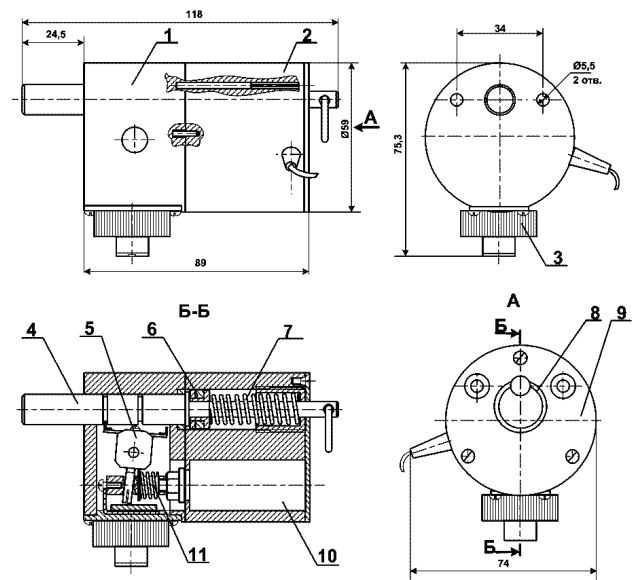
Конструкция: 1 – основание, 2 – цилиндр, 3 – устройство аварийного деблокирования, 4 – шток, 5 – механизм блокировки, 6 – магнит, 7 – пружина, 8 – кольцо, 9 – крышка, 10 – электромагнит, 11 – пружина
